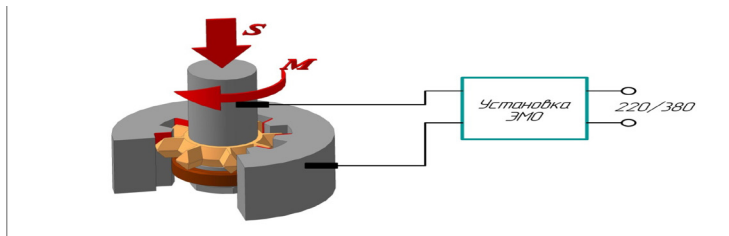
Схема процесса электрохимической закаливания рабочих поверхностей шлицевой втулки
